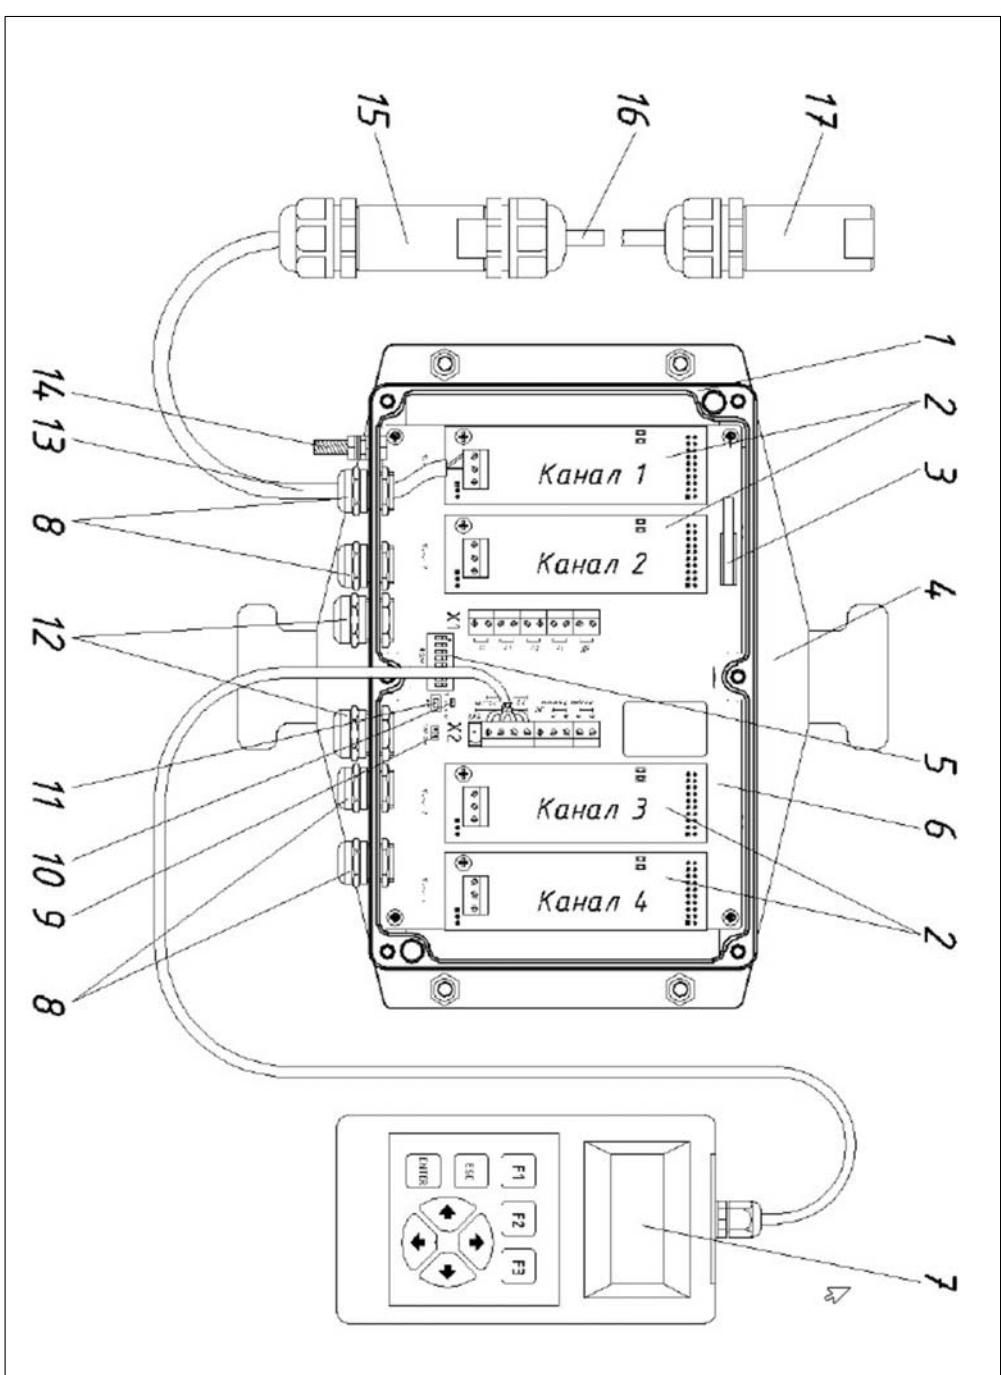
Внешний вид извещателя (вид без крышки БОС)
